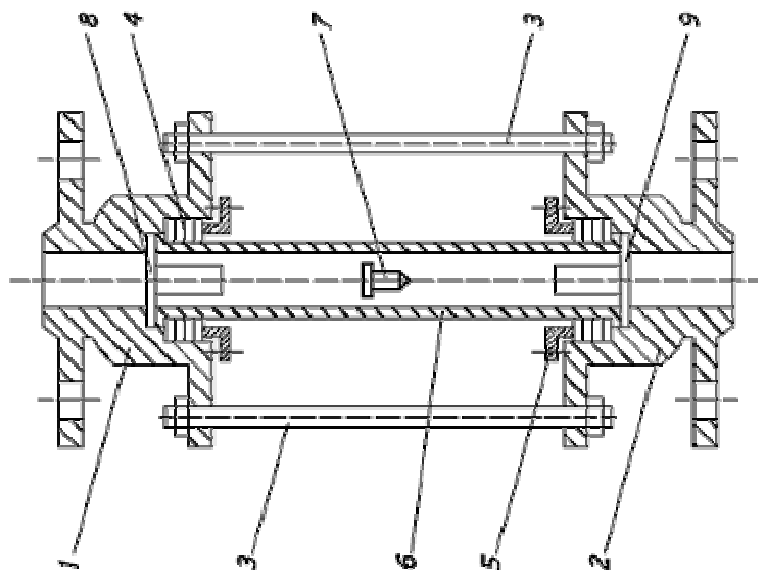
Схема ротаметра: 1 - верхній патрубок, 2- нижній патрубок, 3- болтові стрижні, 4-накидні гайки, 5-сальний ущільнювач, 6-скляна трубка, 7-поплавець, 8-верхній упор, 9-нижній упор
